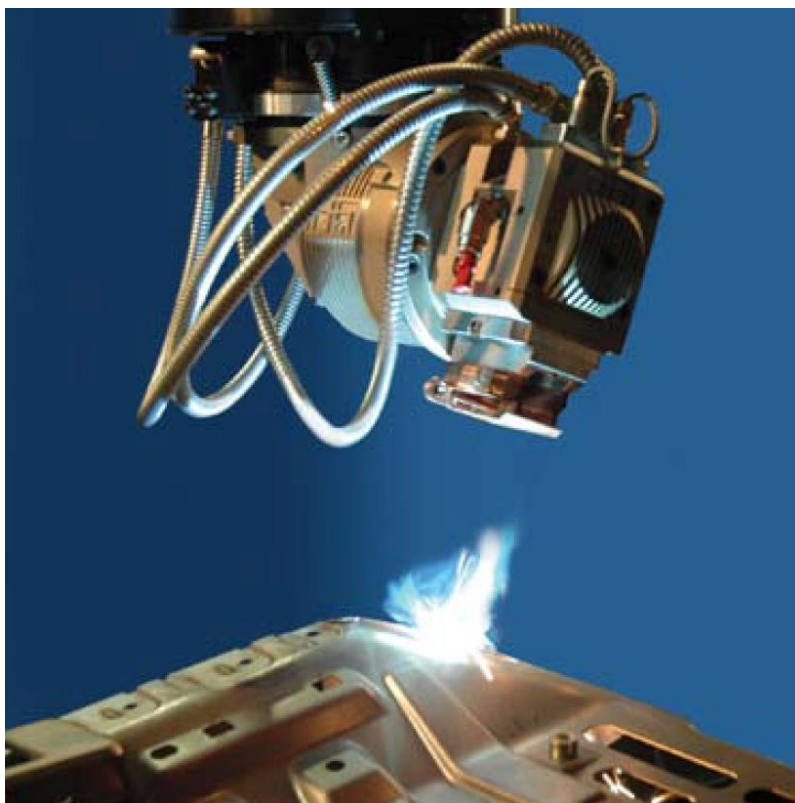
Процесс лазерной сварки конструкции воздушного судна
